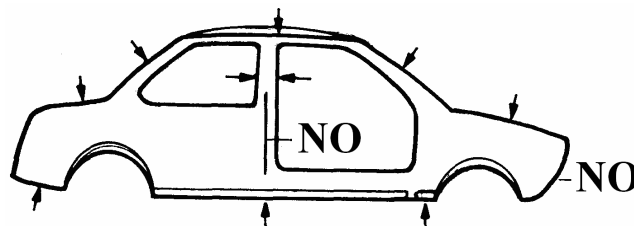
Puntos de destrucción de soldadura.
